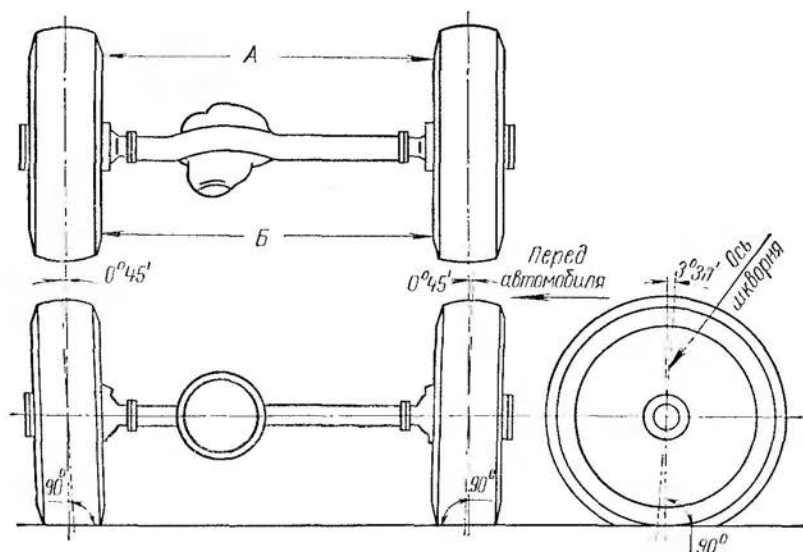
Углы установки передних колес автомобиля ГАЗ-66
